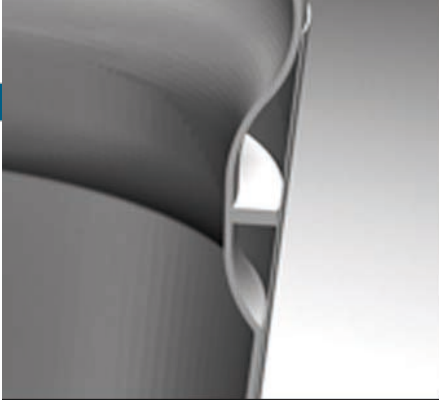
Schnittansicht einer in zwei Teilen thermogeformten Kunststoffflasche mit optimal ausgelegter und durch Etikette verdeckter Schweißnaht. Oben Schweißnaht vergrößert.
